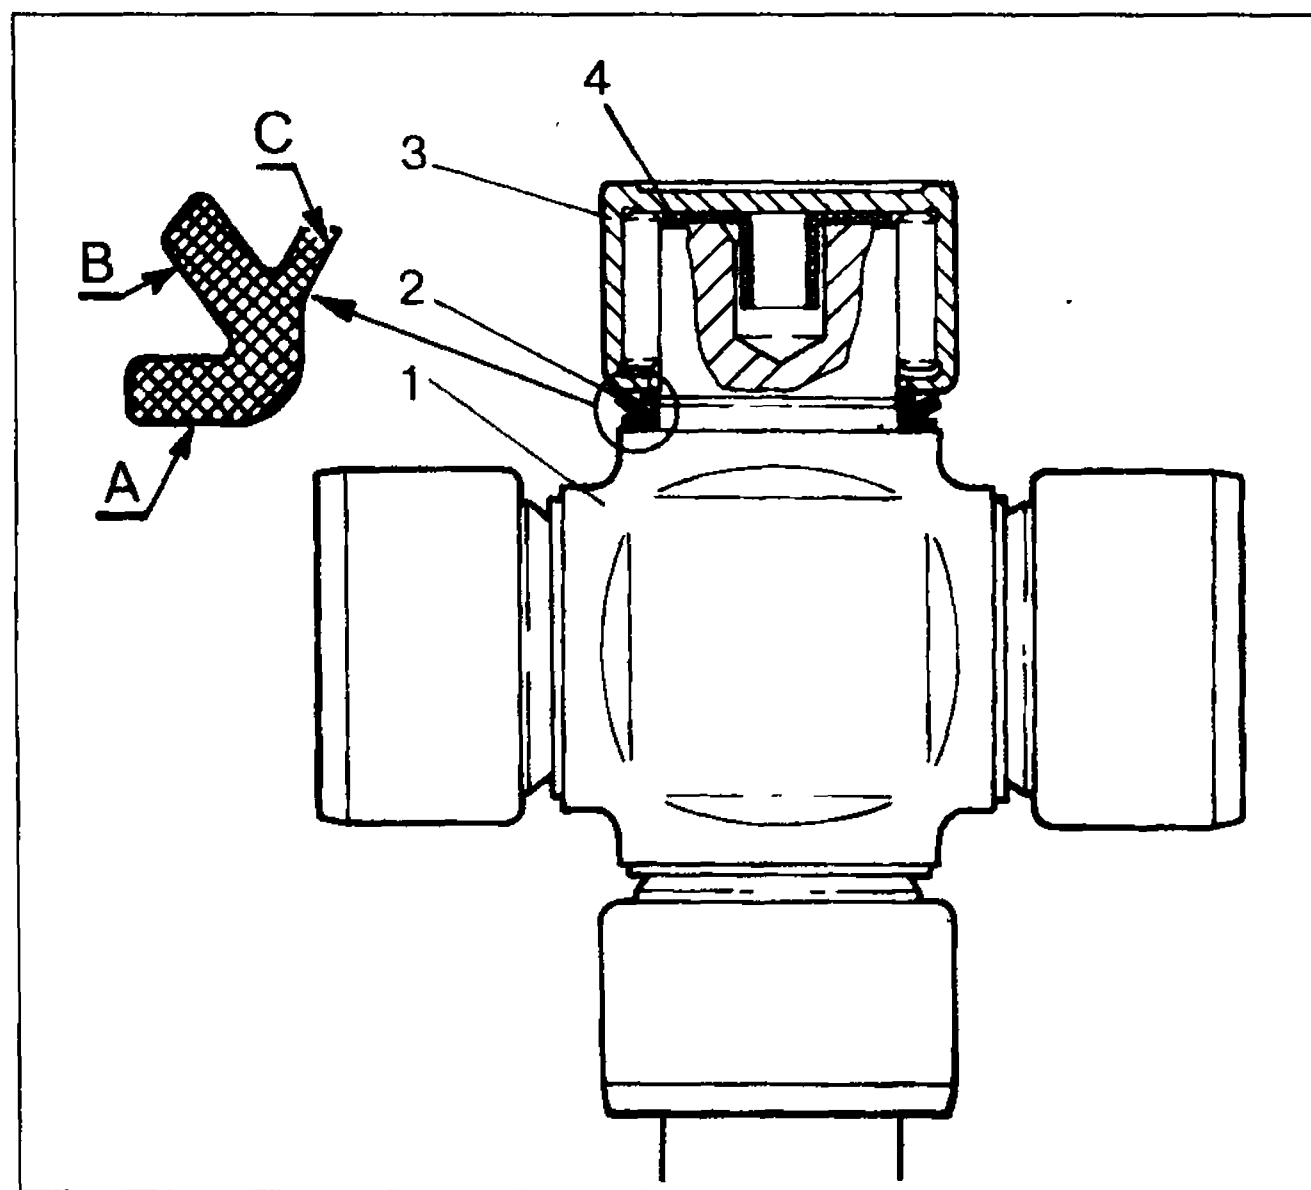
Крестовина карданного шарнира в сборе:
